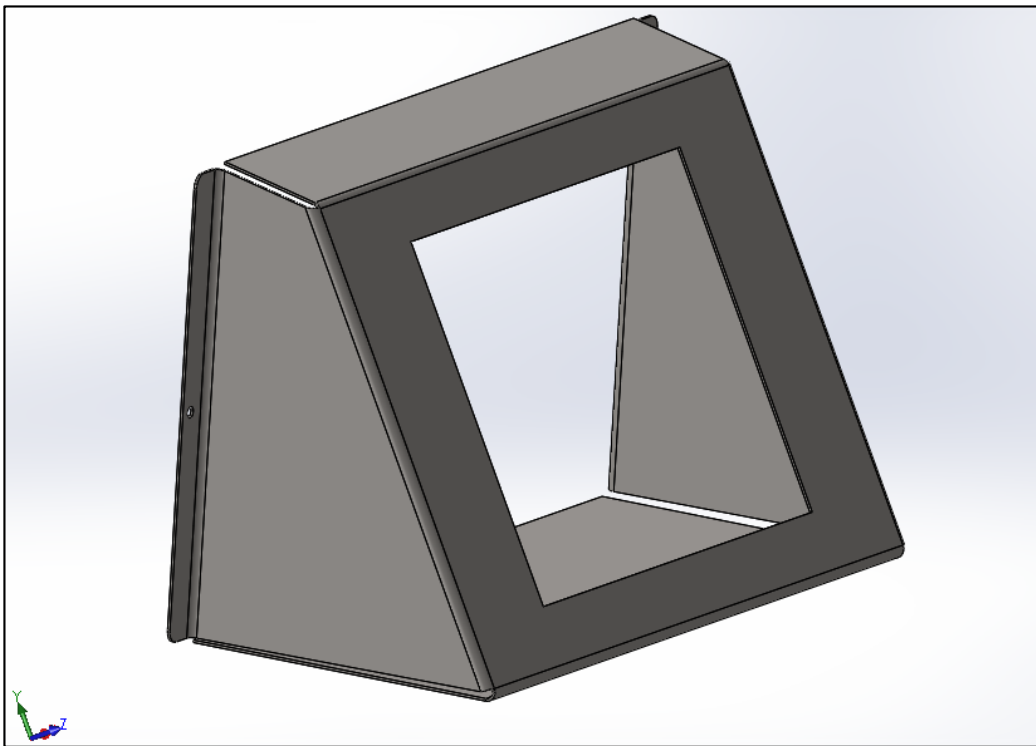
Diseño 3D de chapa metálica para ensamblar pantalla HMI.
